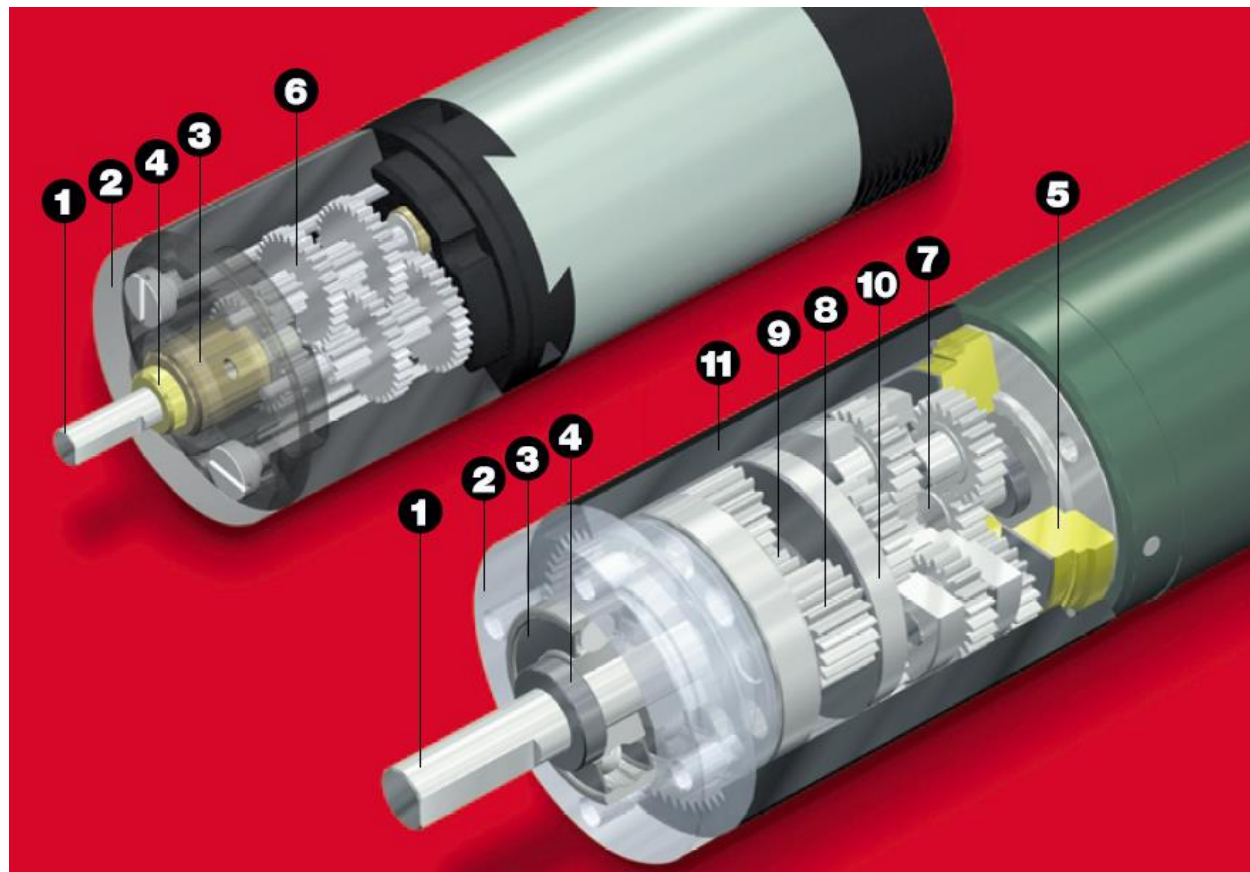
Tren de engranajes planetario en donde se puede observar sus componentes típicos: Sol (sun); brazo o portaplanetas (arm); planeta (planet); engranaje anular (ring gear).
